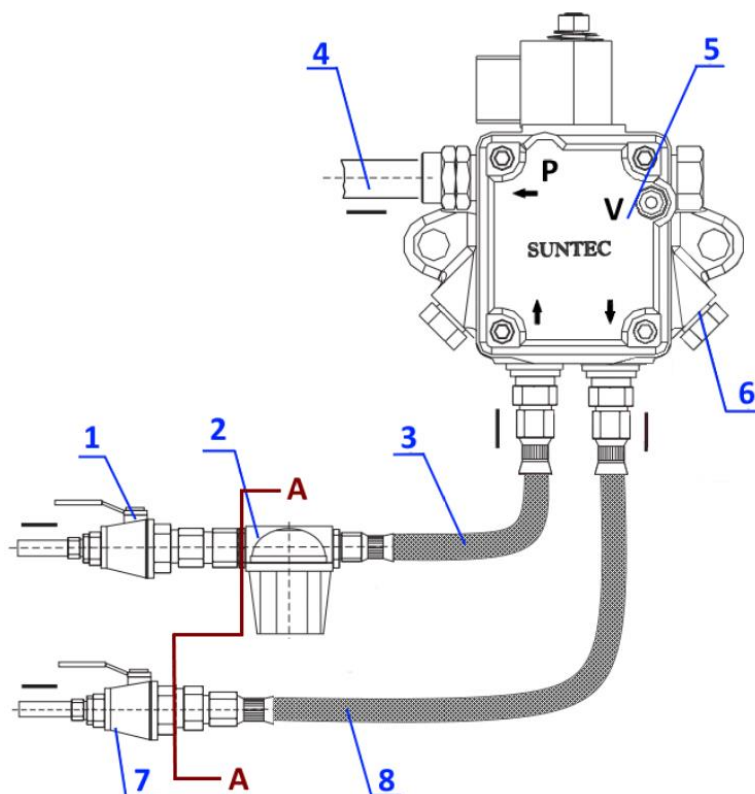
Топливная система горелки. 1 – Запорный кран; 2 – Топливный фильтр; 3 – Гибкий шланг подачи топлива; 4 – Напорная труба к форсунке; 5 – Топливный насос; 6 – Боковой терминал; 7 – Запорный кран; 8 – Гибкий шланг для возврата топлива.
